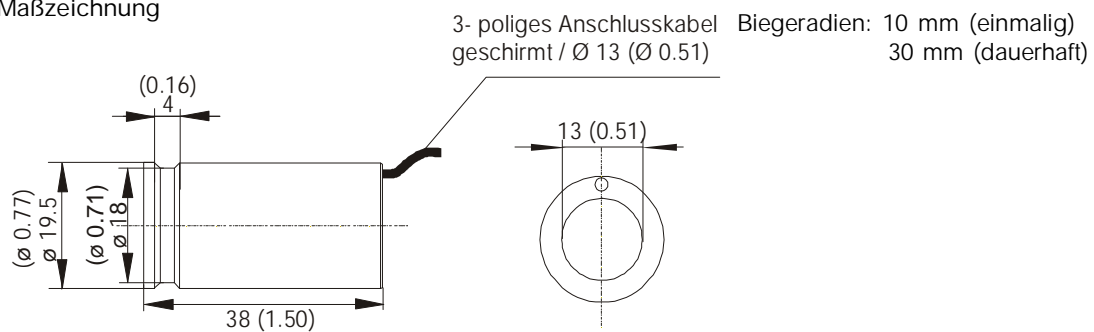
Maßzeichnung Sensor LVP-25
